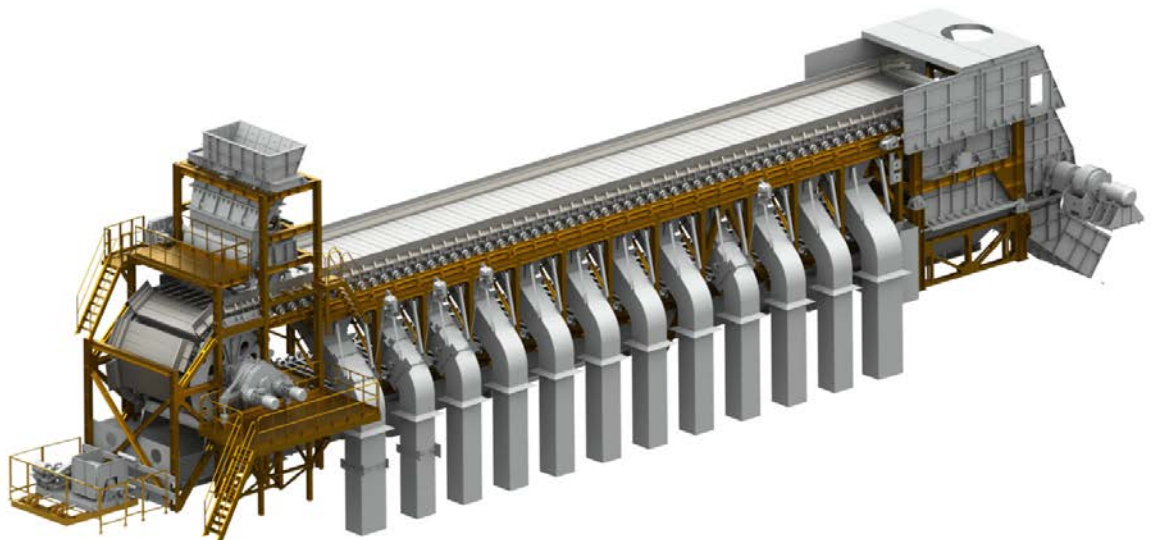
Загальний вигляд агломераційної машини [32]
